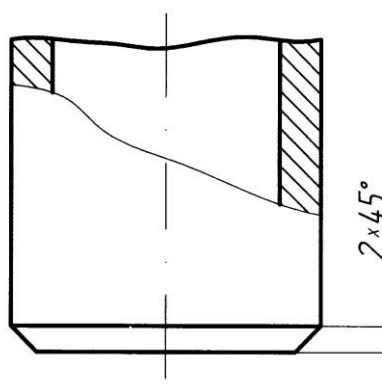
Подготовка кромок трубок под сварку с нижней трубной решеткой
